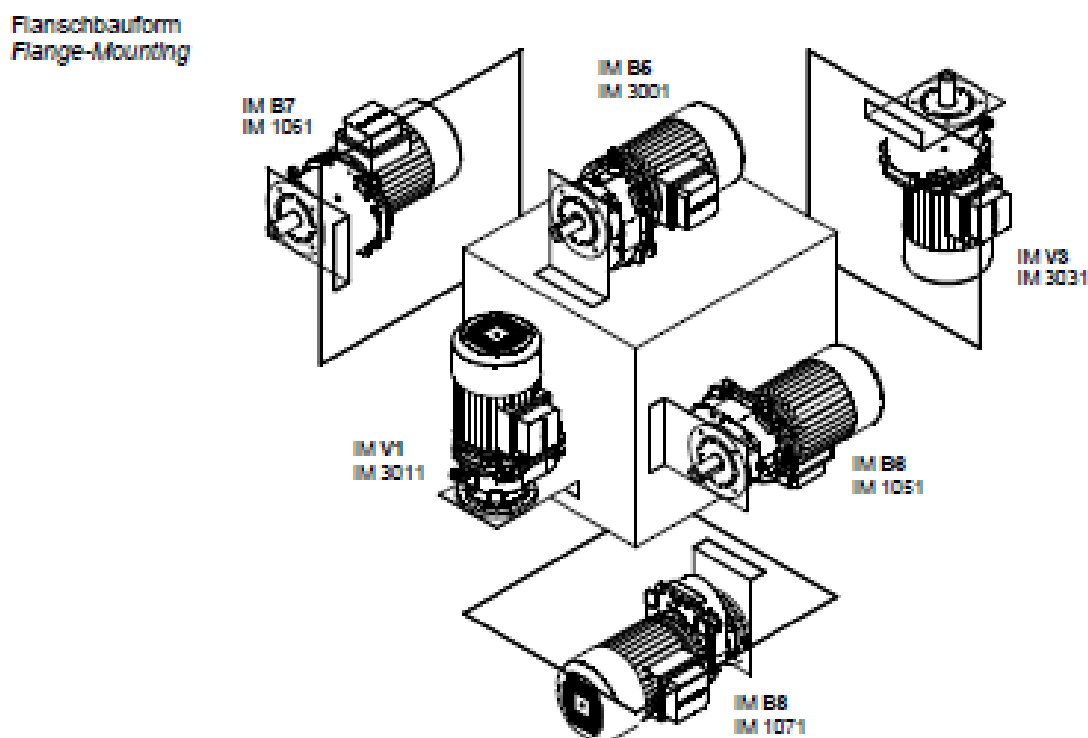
Posições de montagem do redutor e motor eléctrico [10].
